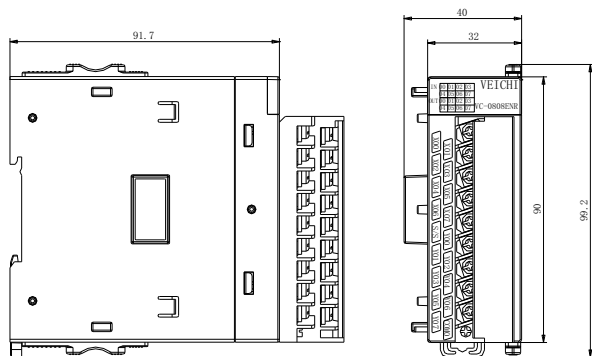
I/O 扩展模块外形尺寸与安装孔位尺寸 (单位: mm)
